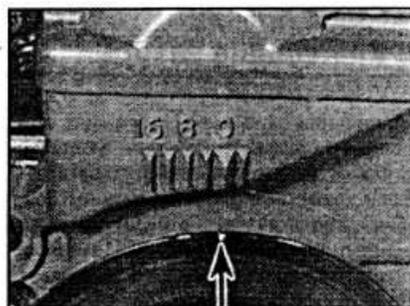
В.3. Метка на шкиве коленчатого вала совмещенная с делением (0) шкалы на крышке зубчатого ремня.
